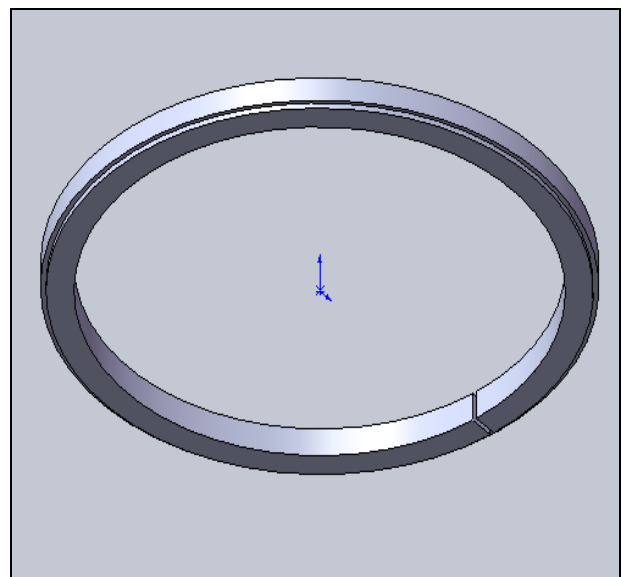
Кольцо скребкового типа (вид снизу)
